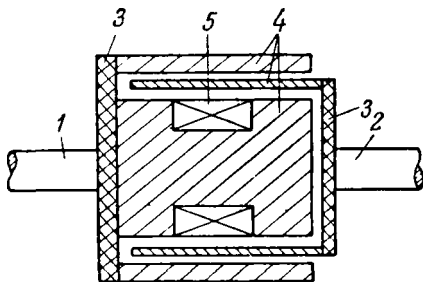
Схема магнитоэмulsionной муфты с несколькими поверхностями трения.
